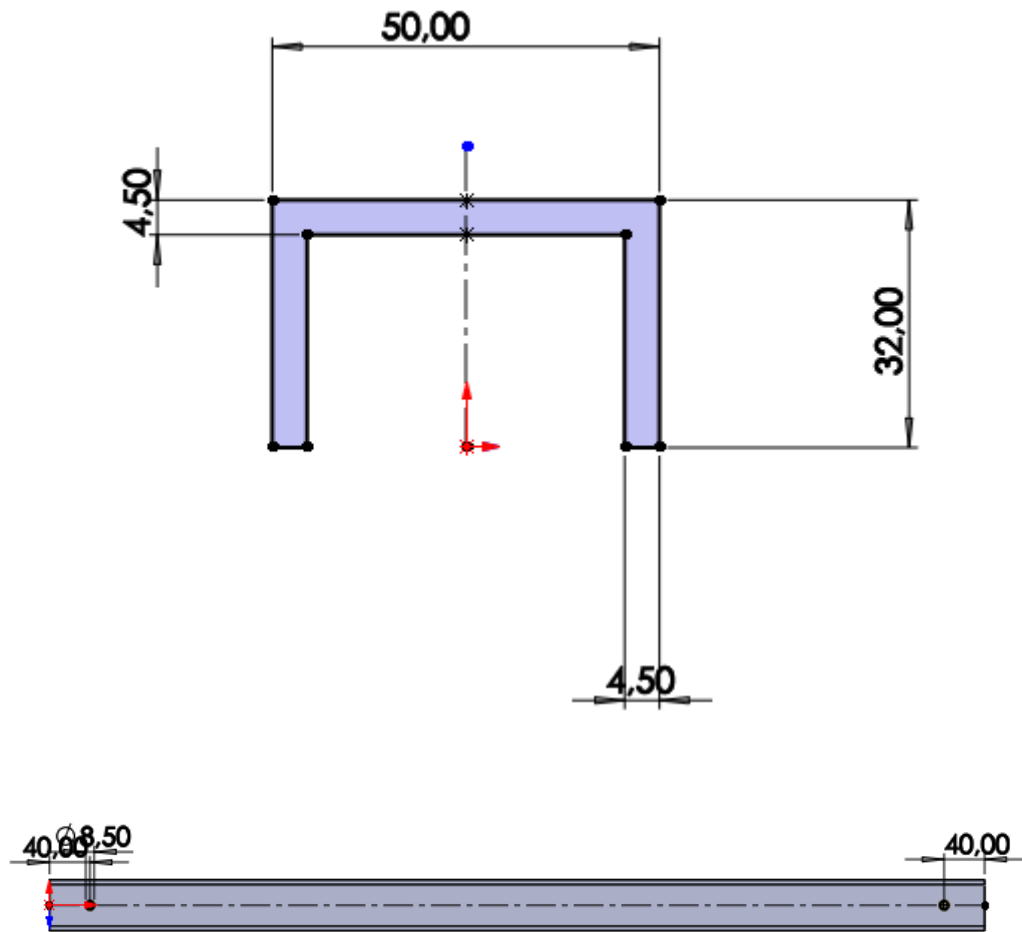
Эскиз для выполнения следующей части детали 23: швеллер
